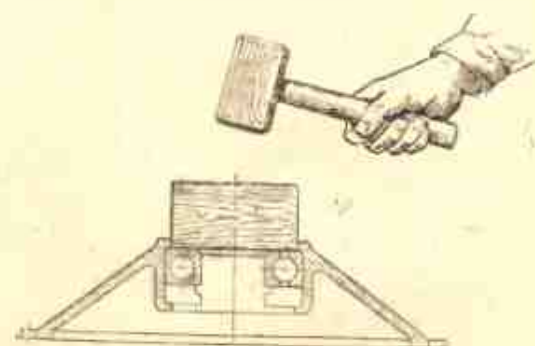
Посадка упорного шарикоподшипника в носовую часть картера
